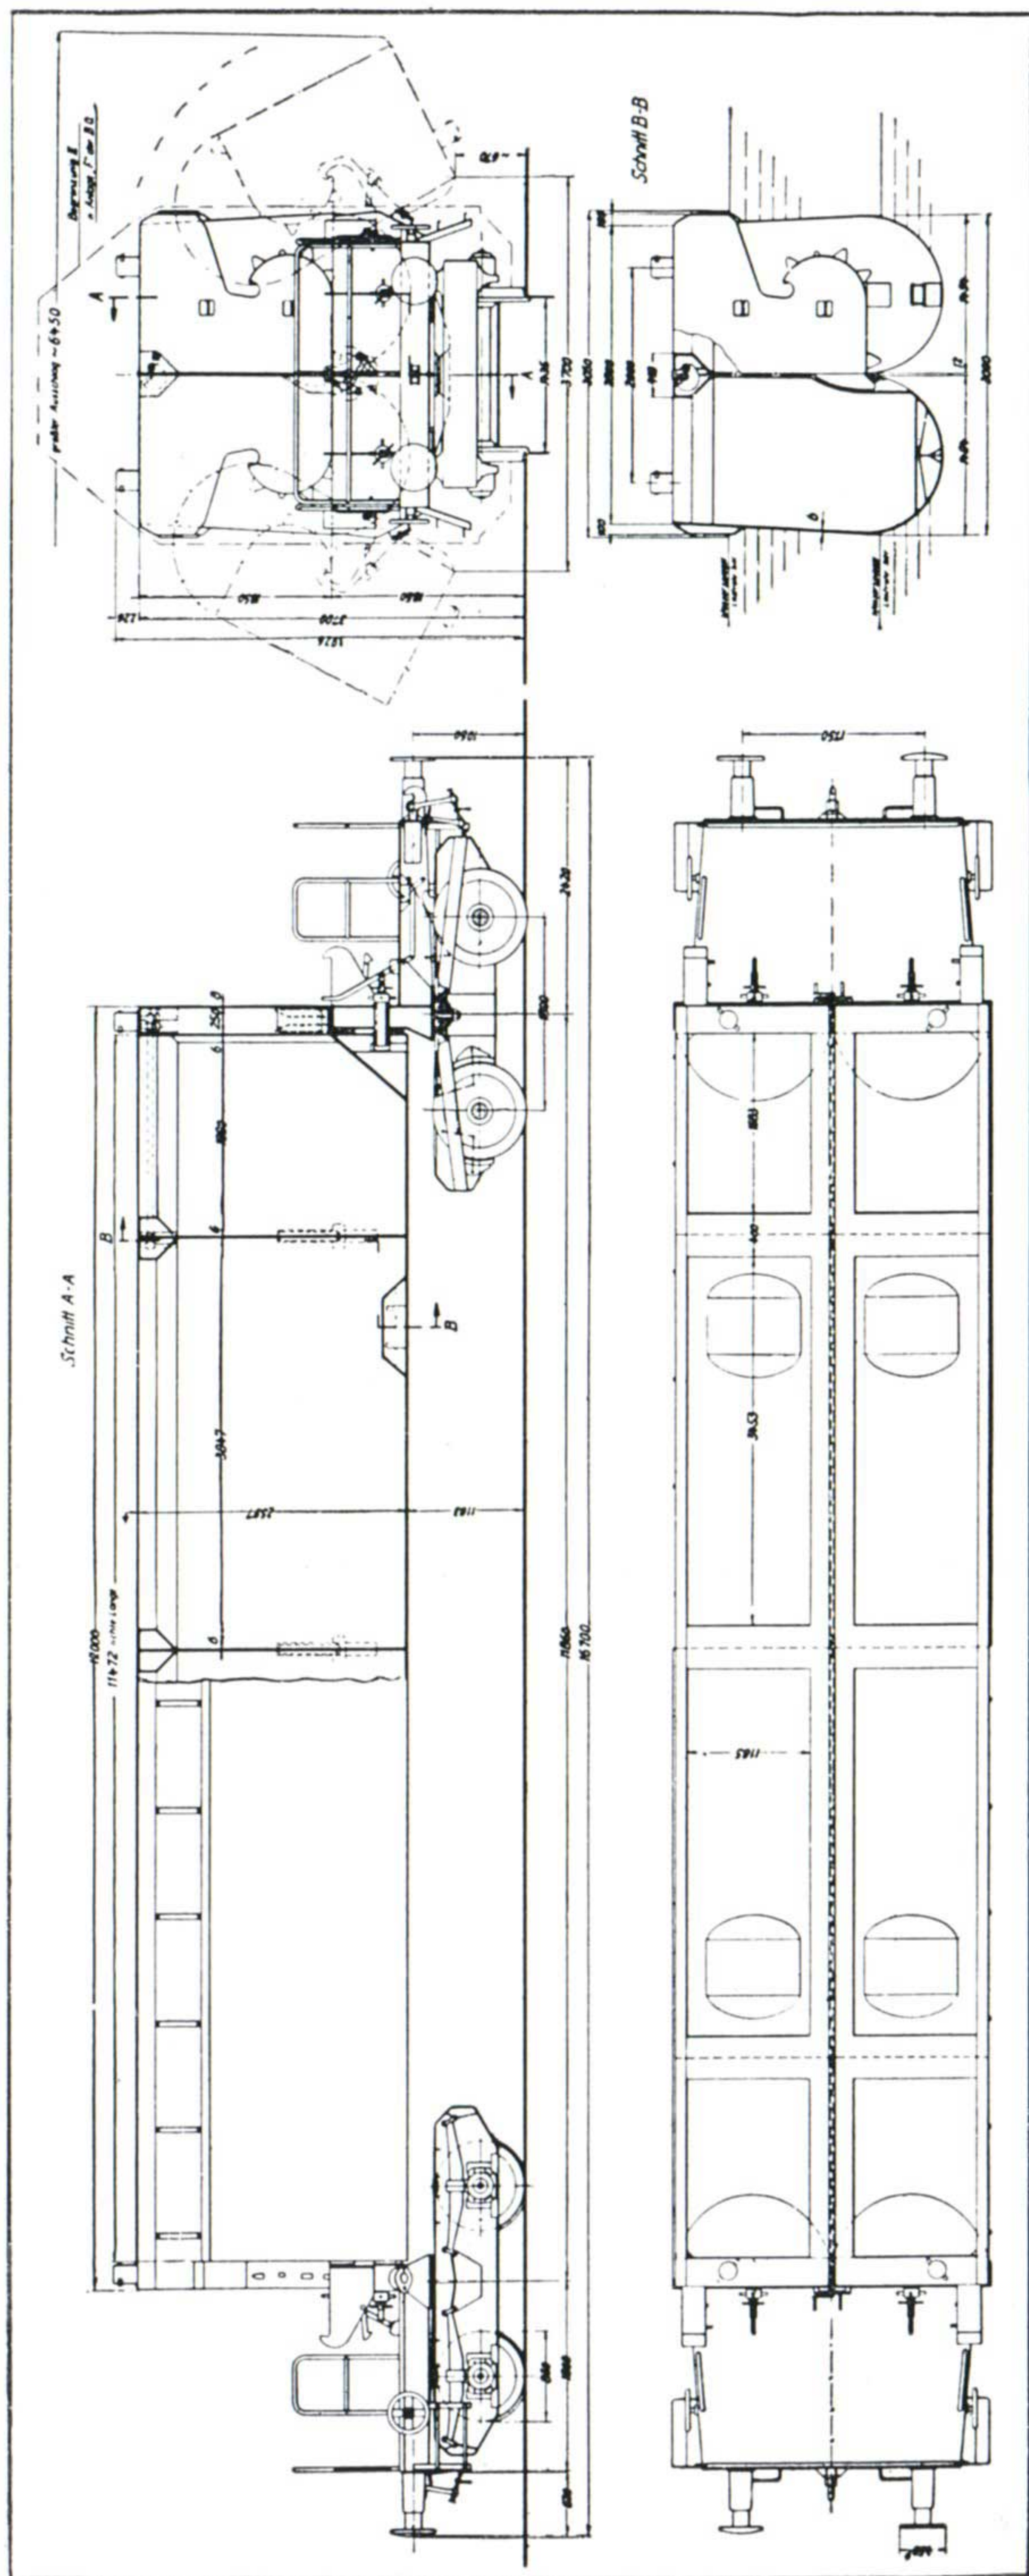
Schéma du deuxième type de caisson monté sur ses bogies, construit par Orenstein-Koppel & Lübecker Maschinenbau A.G. — Coupe, profil et vue de dessus. (Cliché R.N.I.R.)
